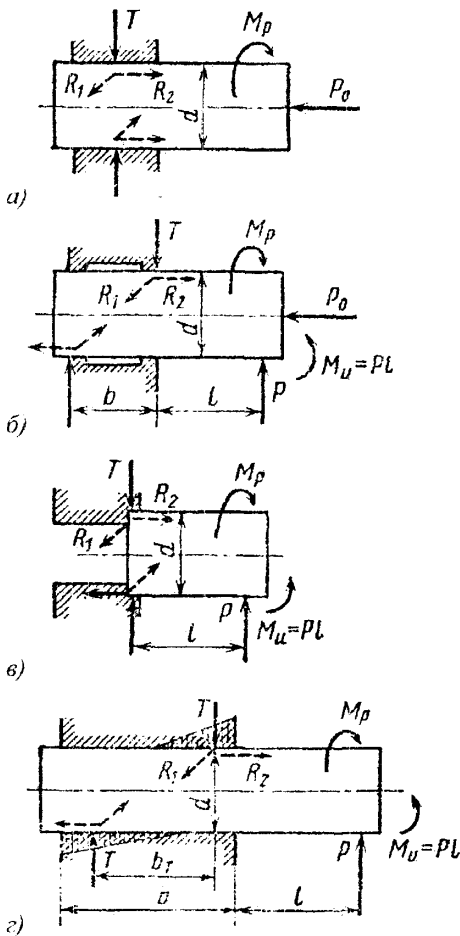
Схемы закрепления и нагружения вращающегося объекта: а – при сверлении; б – при сверлении (или консольном фрезеровании); в – при обработке с малой базой зажима; з – при обработке с большой базой зажима
